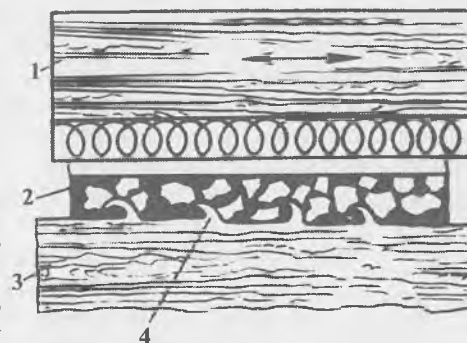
Схема ручного шлифования: 1 — колодка; 2 — шлифовальная шкурка; 3 — обрабатываемая заготовка; 4 — срезаемая стружка
